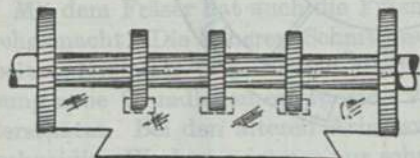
Gruppenfräser zum Fräsen eines Schlittens mit Spannuten.
